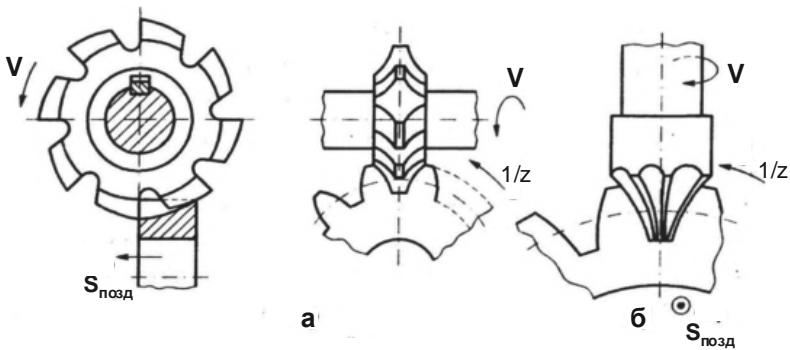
Схеми фрезерування зубів зубчастих коліс методом копіювання: а – дисковою модульною фрезою; б – пальцевою модульною фрезою;  $S_{\text{позд}}$  – поздовжня подача;  $z$  – число зубів;  $1/z$  – частина оберту зубчастого колеса
